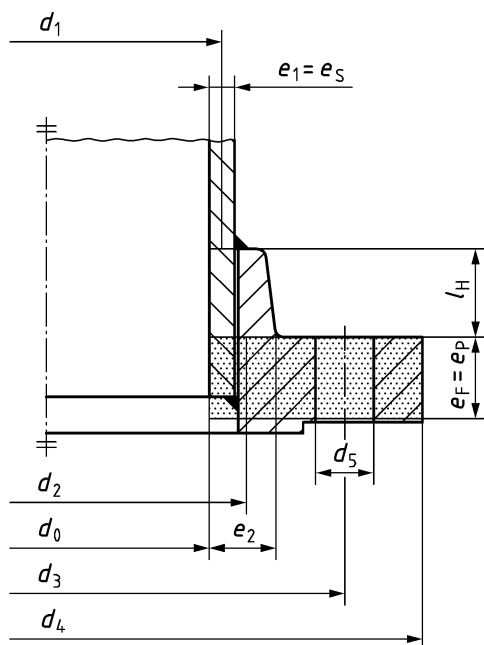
Überschieb-Schweißflansch mit Ansatz
